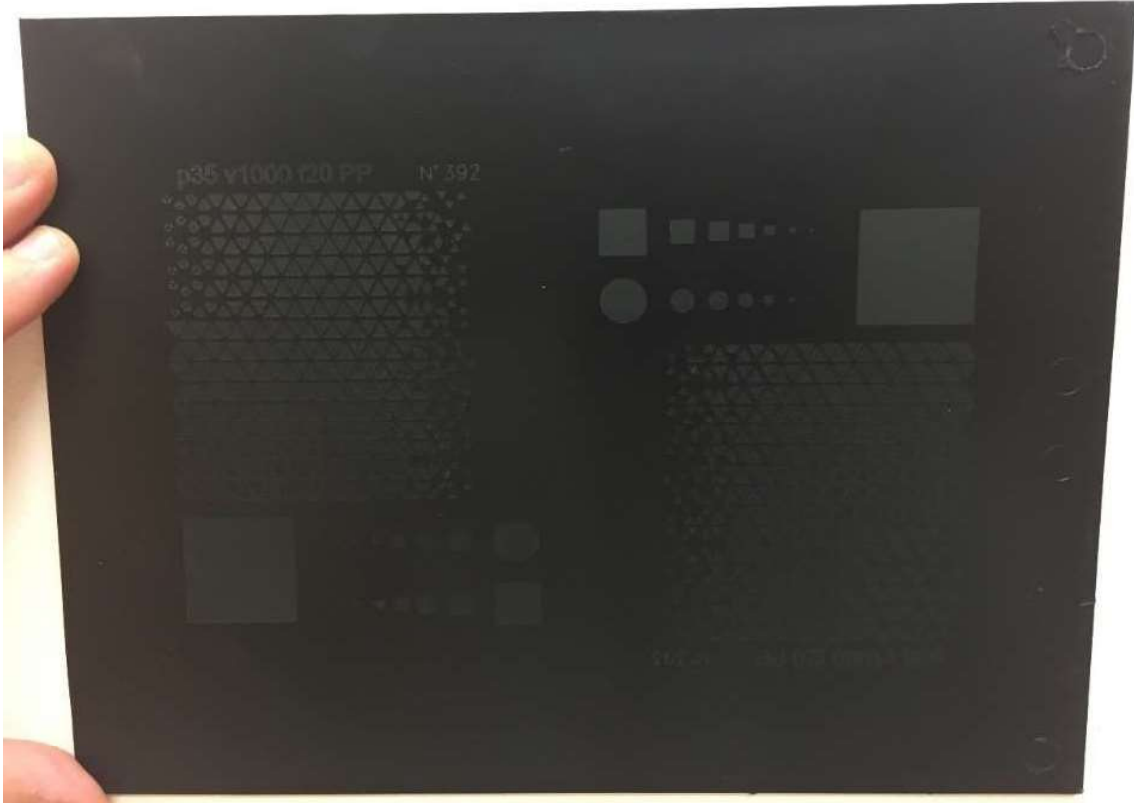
Éprouvette de travail gravée par laser (zones mates).
